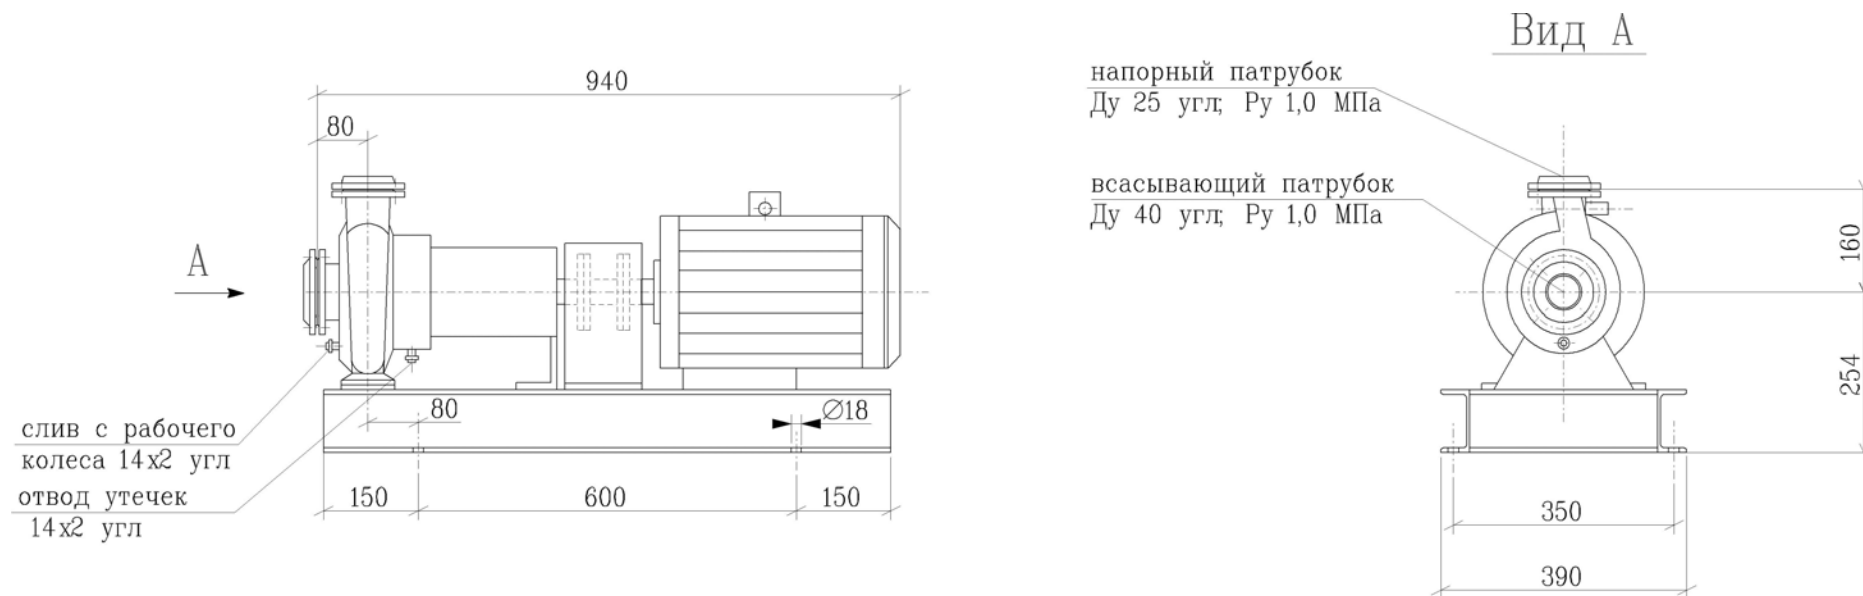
Габаритный чертеж насоса фосфата QCT10AP001, QCT10AP002
